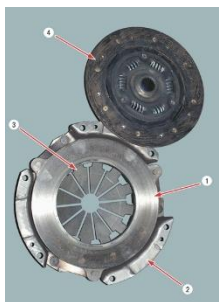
Сцепление в разобранном виде: 1—нажимной диск; 2—кожух сцепления; 3—диафрагменная пружина; 4—ведомый диск
